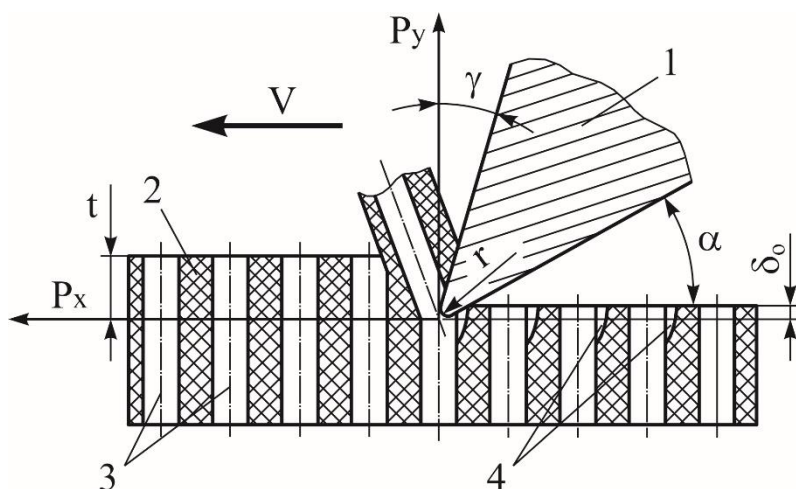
Кінематична схема утворення тріщин поверхневого шару композиту: 1 – ріжучий клин зі швидкістю V ; 2 – матриця; 3 – волокно; 4 – зона утворення тріщини біля волокон
